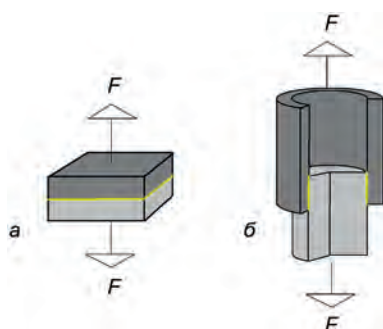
Эскизы образцов для испытаний сварного соединения: а – на разрыв; б – на срез
